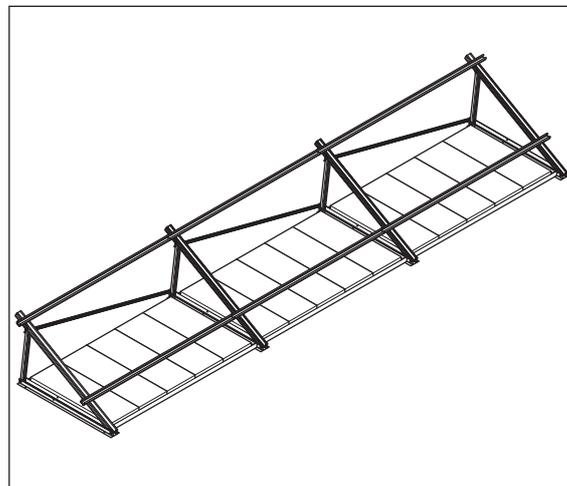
Ejemplo de bastidor de tejado plano para 3 colectores planos (EKSH26P)
